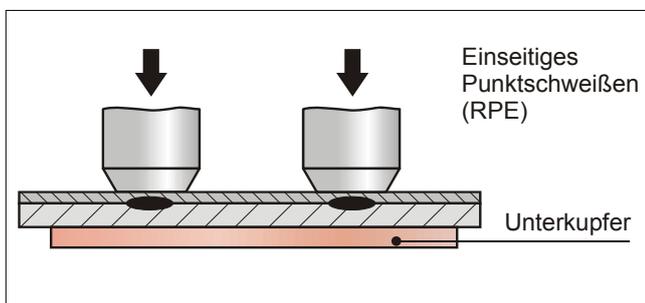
Prinzip des einseitigen Widerstandspunktschweißens aus [1]
